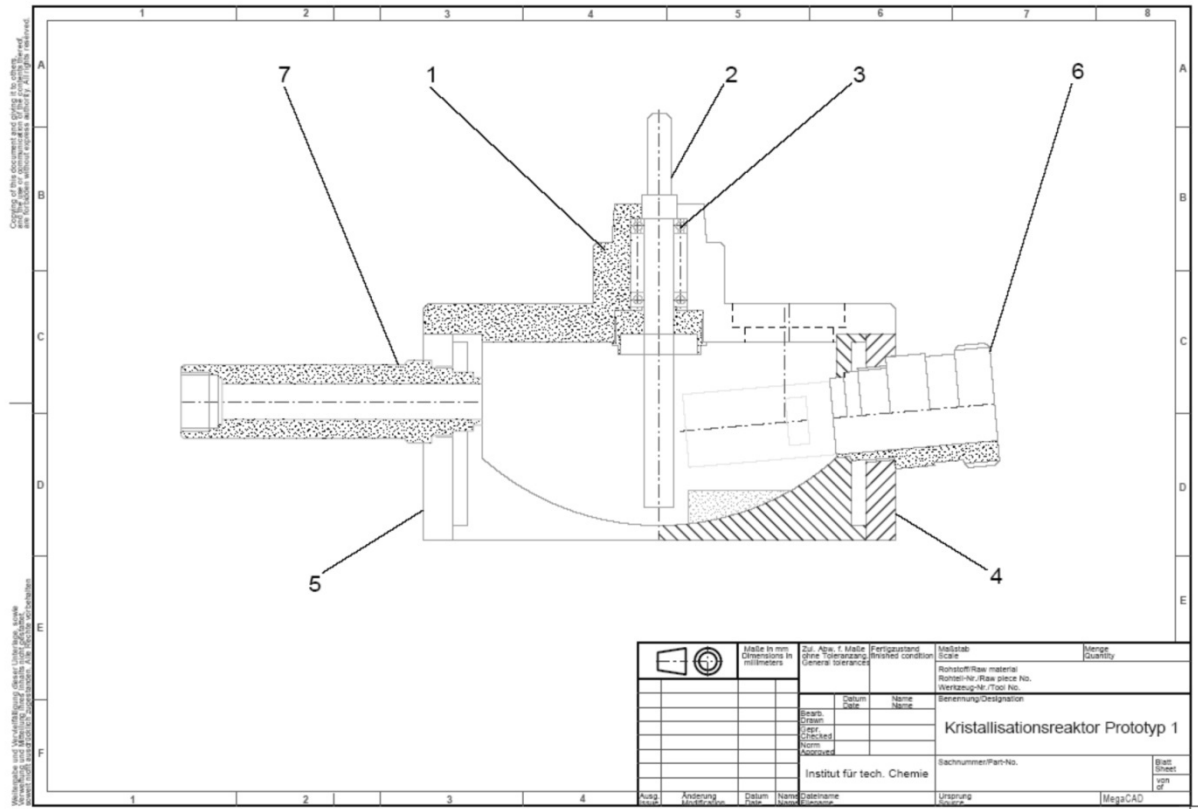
Technische Zusammenbauzeichnung des Prototypen A.
